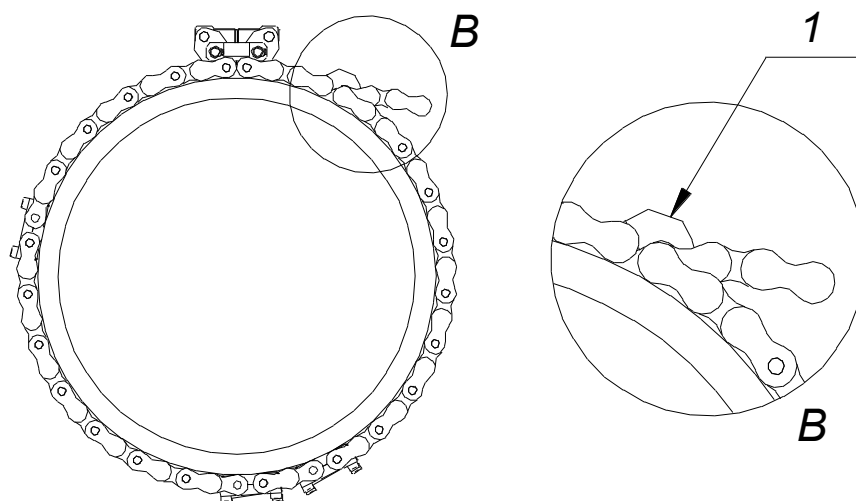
а. Цепь затянута на поверхности трубы: 1 – зацеп
